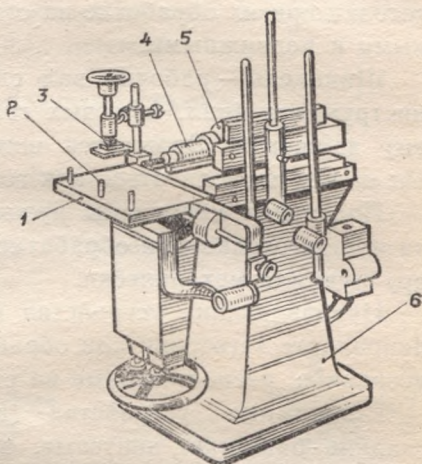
Горизонтальный сверлильно-пазовальный станок:
